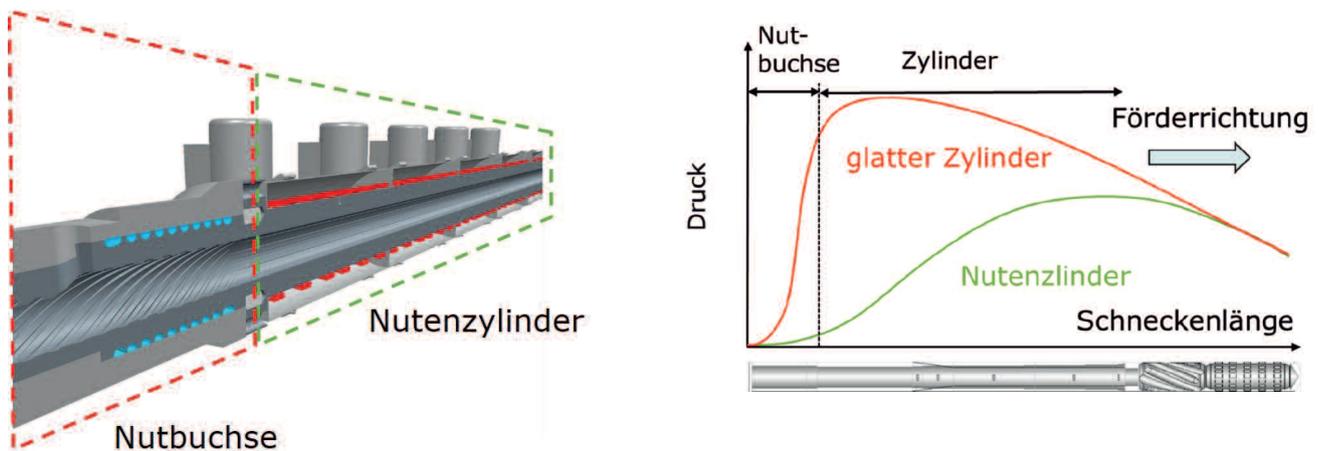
Verfahrenseinheit solEX NG mit Nutenzylinder und Nutbuchse im Schnitt (links) sowie axiales Druckprofil über der Schneckenlänge für einen glatten bzw. genuteten Zylinder (rechts)
